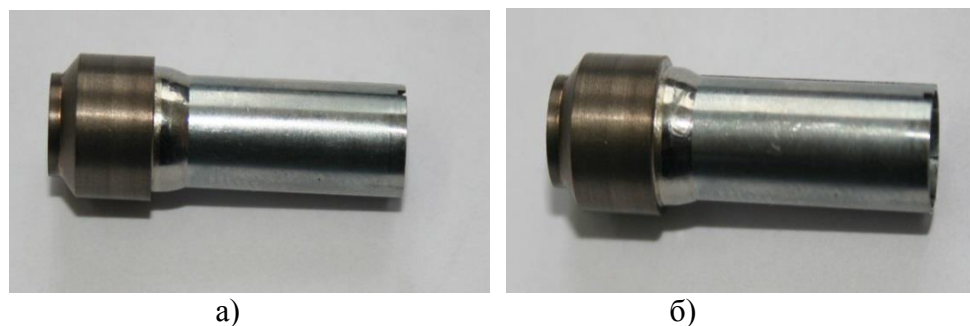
Внешний вид сварочных образцов, сваренных на: а) ЭЛУ-5, б) EVOBEAM - 400
